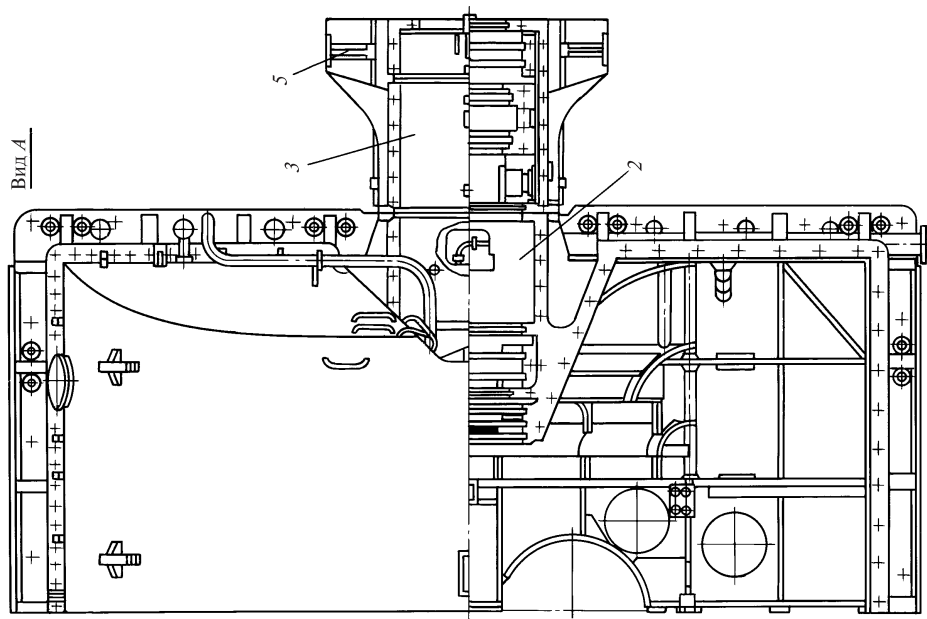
Опираие корпусов ЦВД турбин ХТЗ на корпус подшипника
